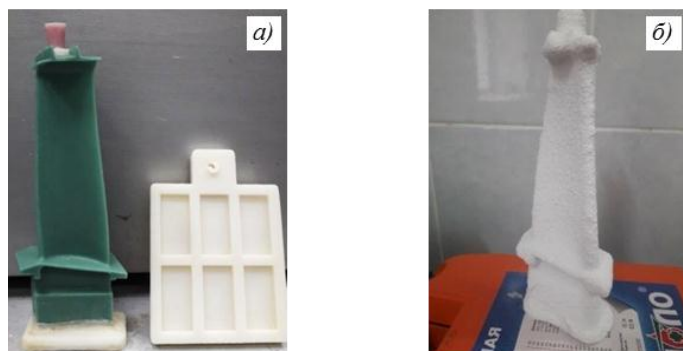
Общий вид восковой модели прототипа лопатки и пластины для изготовления керамических образцов (а) и керамической формы прототипа лопатки до удаления восковой композиции (б), изготовленной на основе связующего золя оксида иттрия
